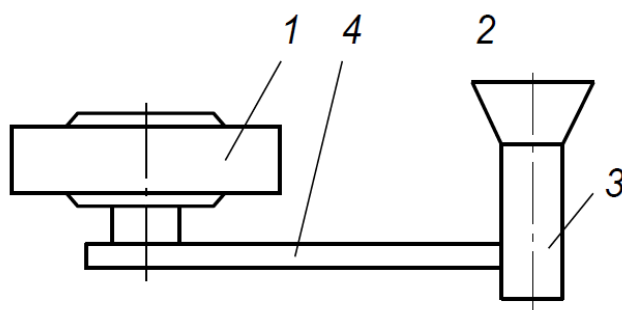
Блок отливки шестерни: 1 – отливка; 2 – верхняя прибыль; 3 – стояк; 4 – питающий коллектор
